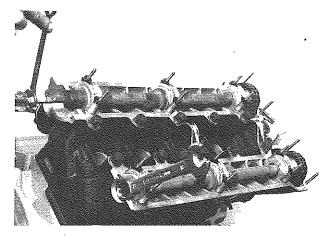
Ruotare gli assi a camme Rotate camshafts
